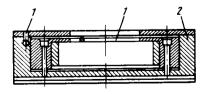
Слесарный уровень: 1 — ампула; 2 — корпус
